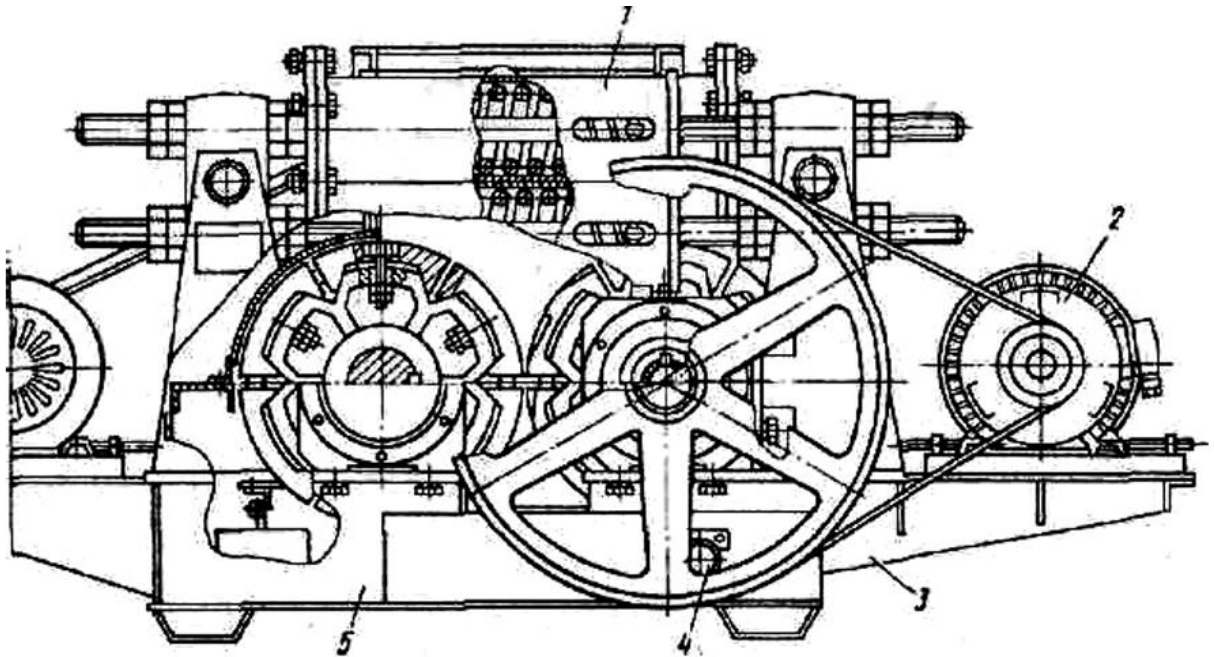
Двухвалкова дробарка з роздільним приводом
